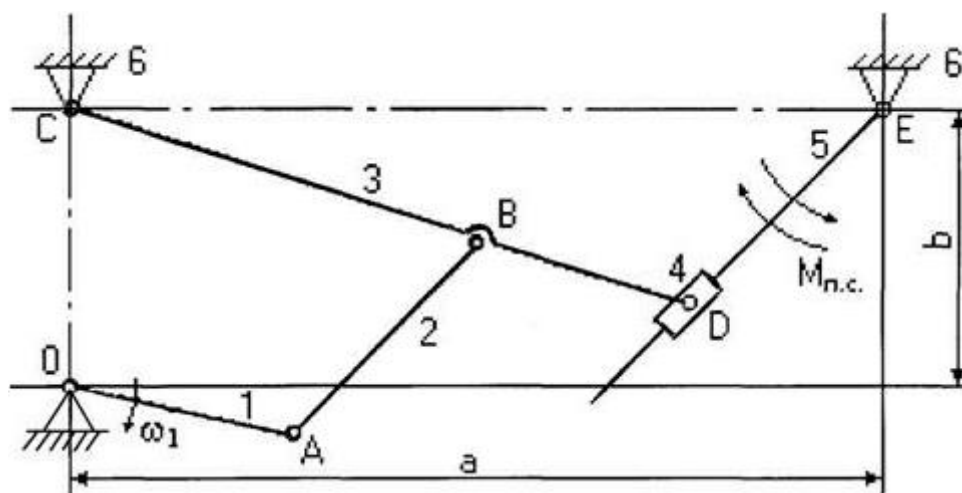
Кинематическая схема плоского рычажного механизма
